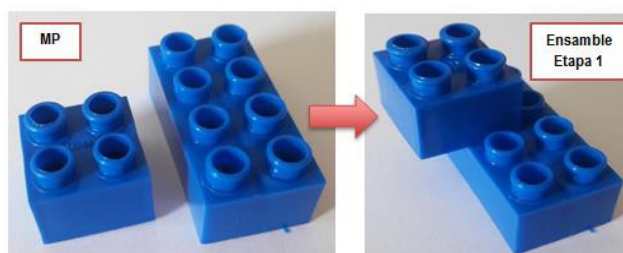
Sub producto de la primera etapa de montaje del diseño de experimento – Fuente: Elaboración propia.
